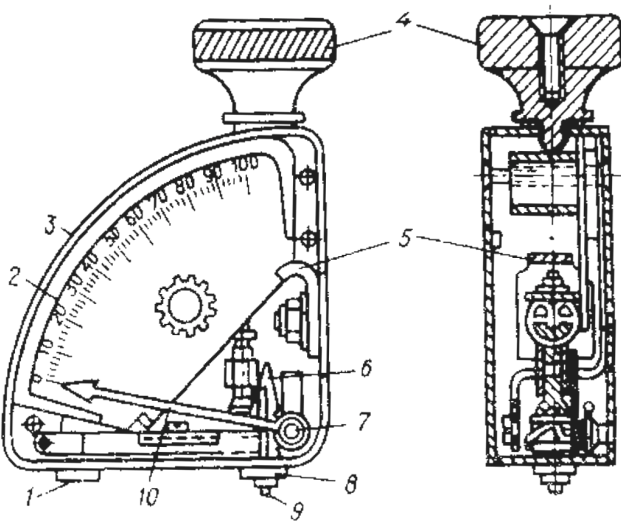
Твердомір ТМ-2: 1 – пластина; 2 – шкала; 3 – корпус; 4 – головка; 5 – пружина; 6 – зубчаста рейка; 7 – шестірня; 8 – шайба; 9 – голка (індентор); 10 – стрілка
